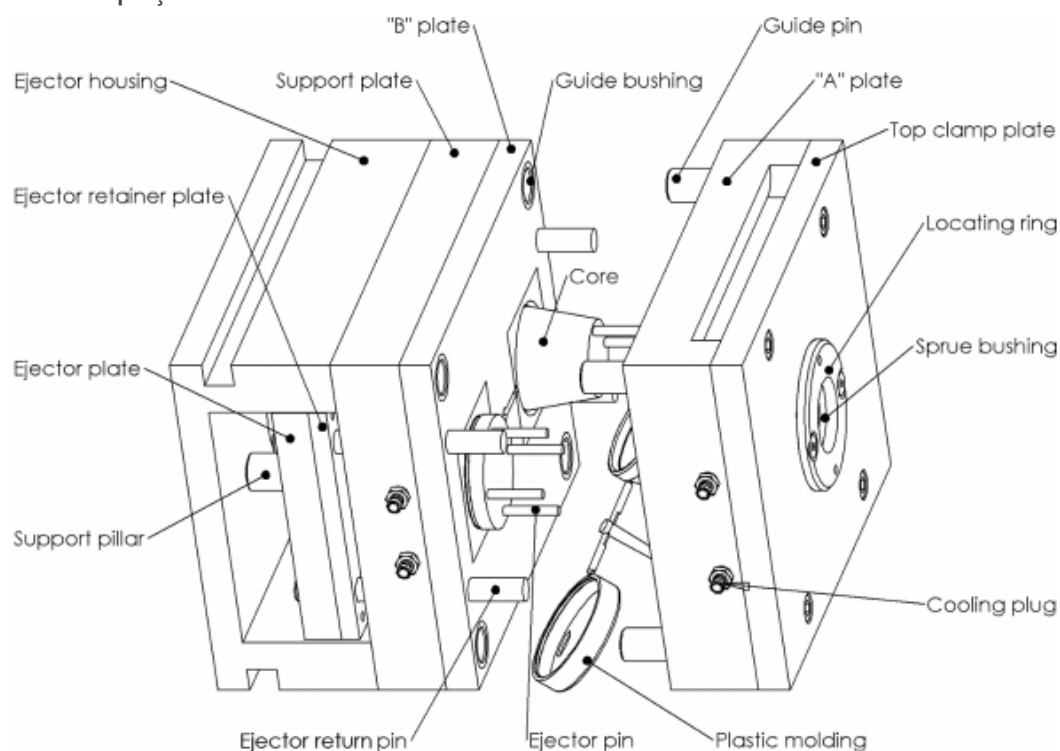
Vista Isométrica de um molde simples de duas placas durante a fase de extração [11]
